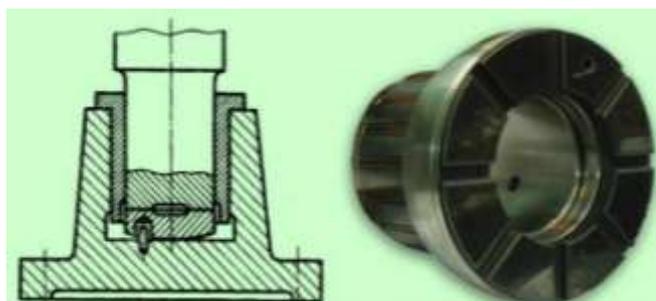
Подпятник (упорный подшипник скольжения)
